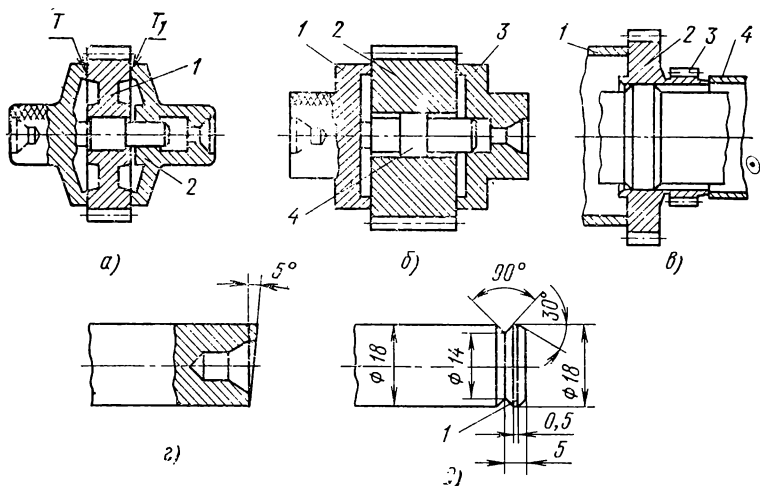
Базирование зубчатых колес при шевинговании (а, б и в), форма заходной части оправки (г и д)
